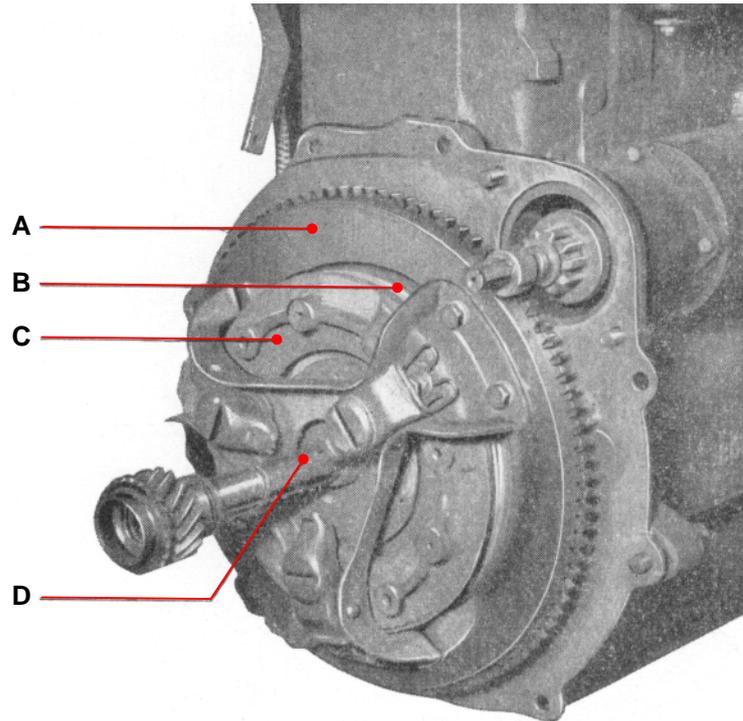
Mise en place du disque et du plateau d'embrayage sur le volant.
